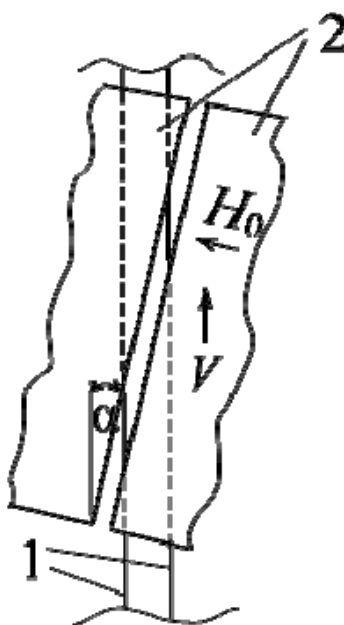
Расположение КМИ при осуществлении способа намагничивания [9]: 1 – контролируемый сварной шов; 2 – пластины прямоугольного сечения
